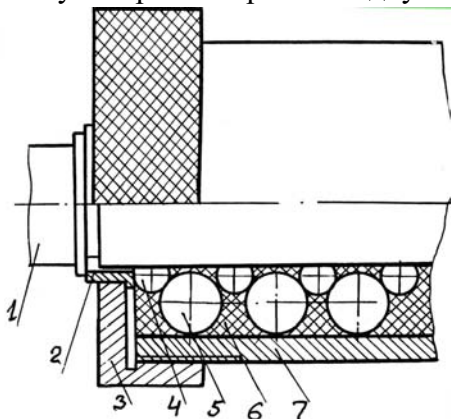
Механізм для закріплення циліндричного інструмента.
